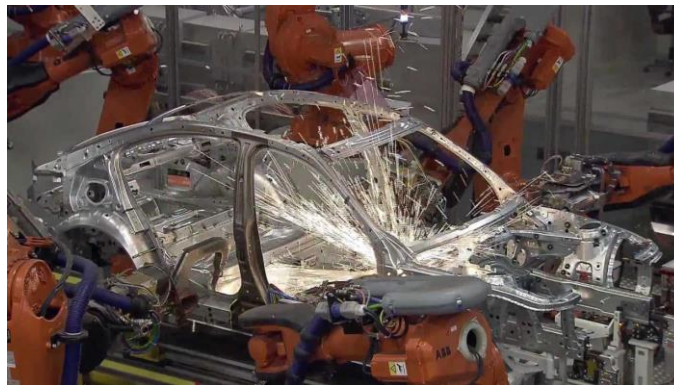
Punktschweißen einer BMW 3er Karosserie (BMW)
